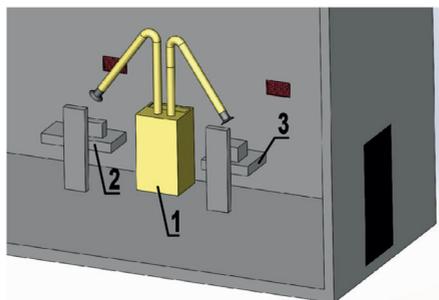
Мобильный фильтр с двумя подъемно-поворотными устройствами:
